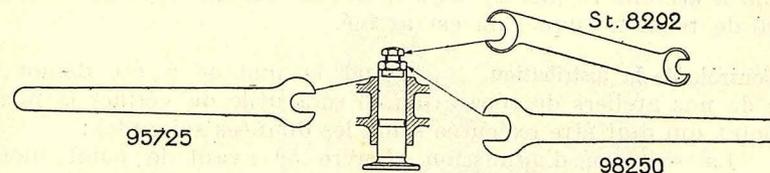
Clefs nécessaires pour le réglage des soupapes.
